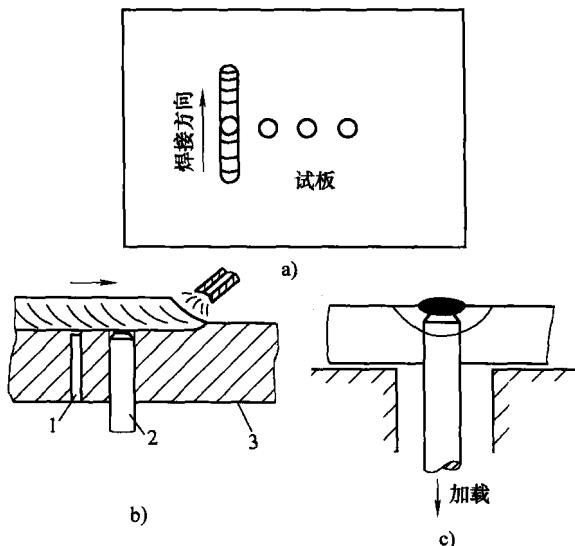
插销试验施焊时焊缝的位置
